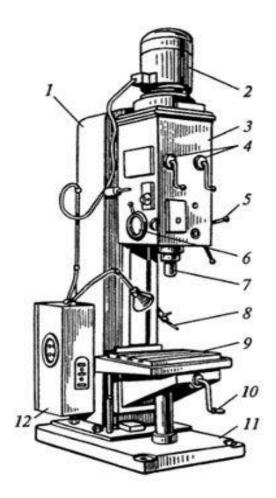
Вертикально-сверлильный станок модели 2H125
